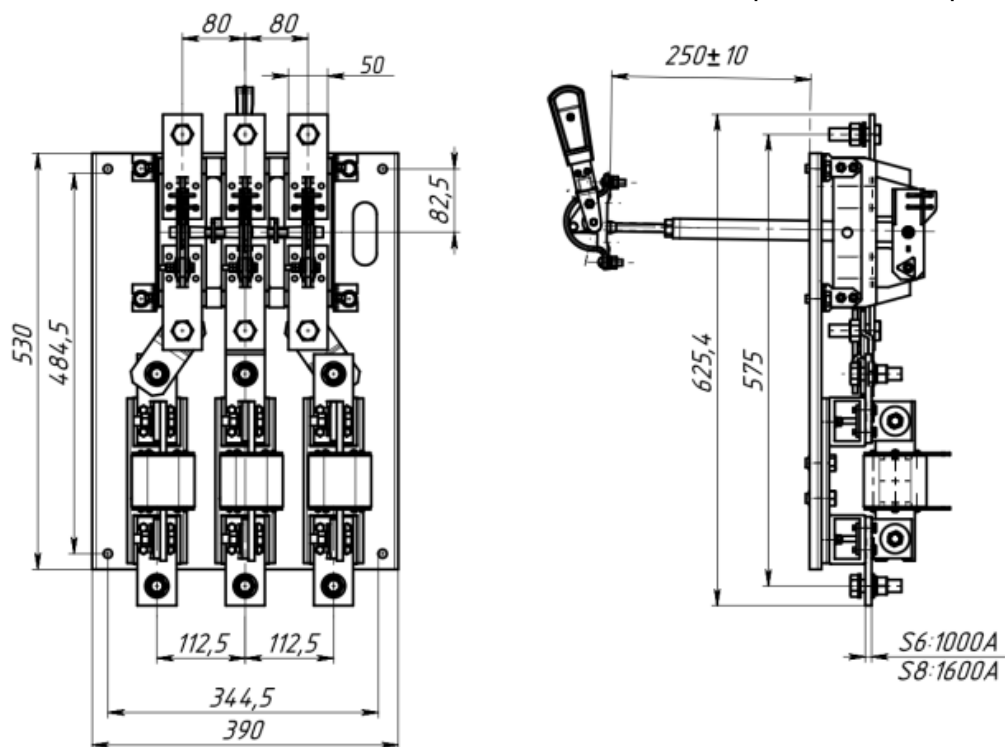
Б Разъединители-предохранители с центральным приводом на токи 1000 А и 1600 А, масса, не более: РПЦ-10 – 26,35 кг; РПЦ-16 – 29,3 кг.
